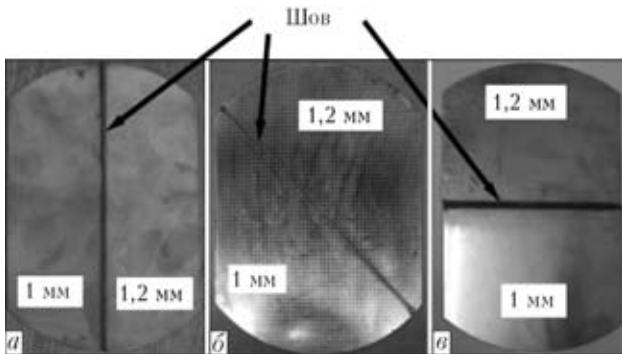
ССЗ (диаметр заготовки 165,1 мм), полученные с различными углами сопряжения элементов: а — 0; б — 45; в — 90°
